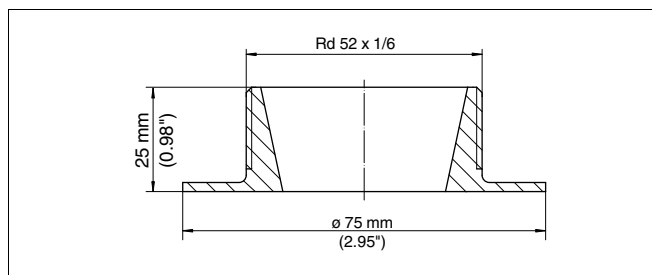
Размеры приварного штуцера для конусного присоединения DN 25
